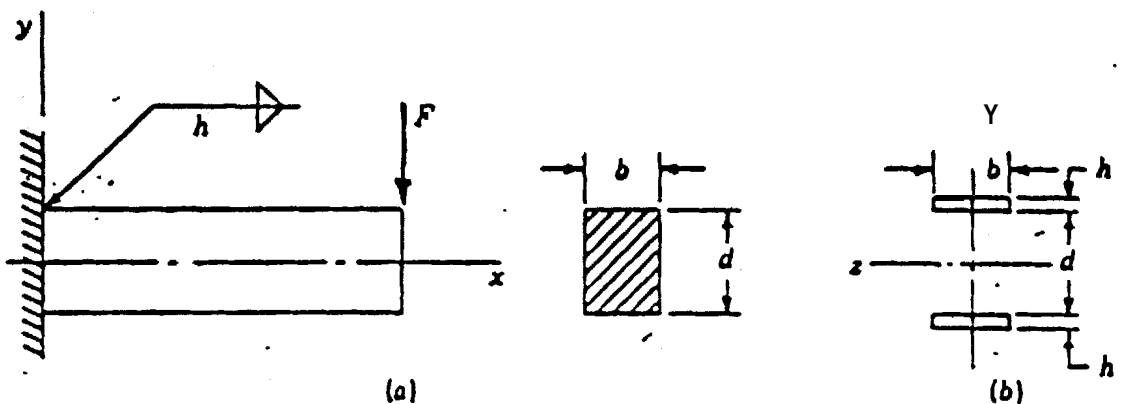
VOLADIZO DE SECCION RECTANGULAR SOLDADO A UN SOPORTE POR LOS BORDES SUPERIOR E INFERIOR DE LA SECCION.(3)
